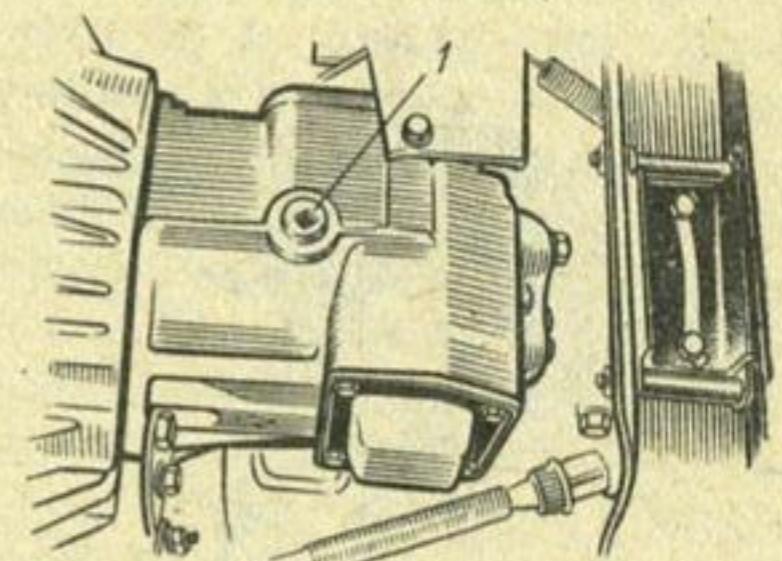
Расположение пробки сливного отверстия картера коробки передач:
